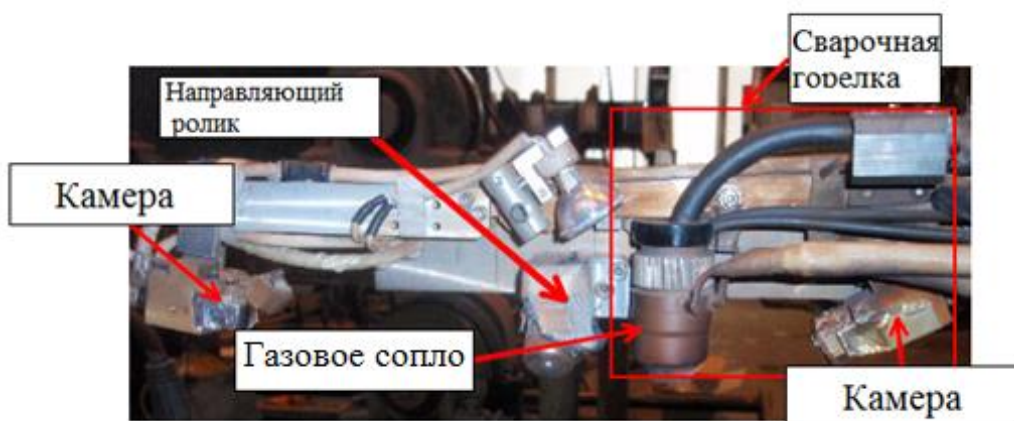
Схема сварочная горелка для узкой части
